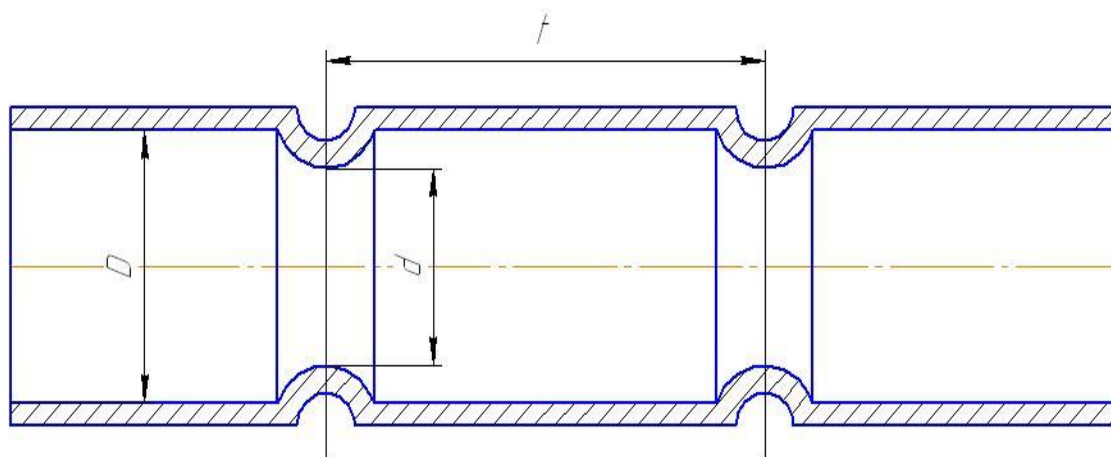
Продольный разрез трубы с зигами на наружной стороне и плавно очерченными выступами внутри
